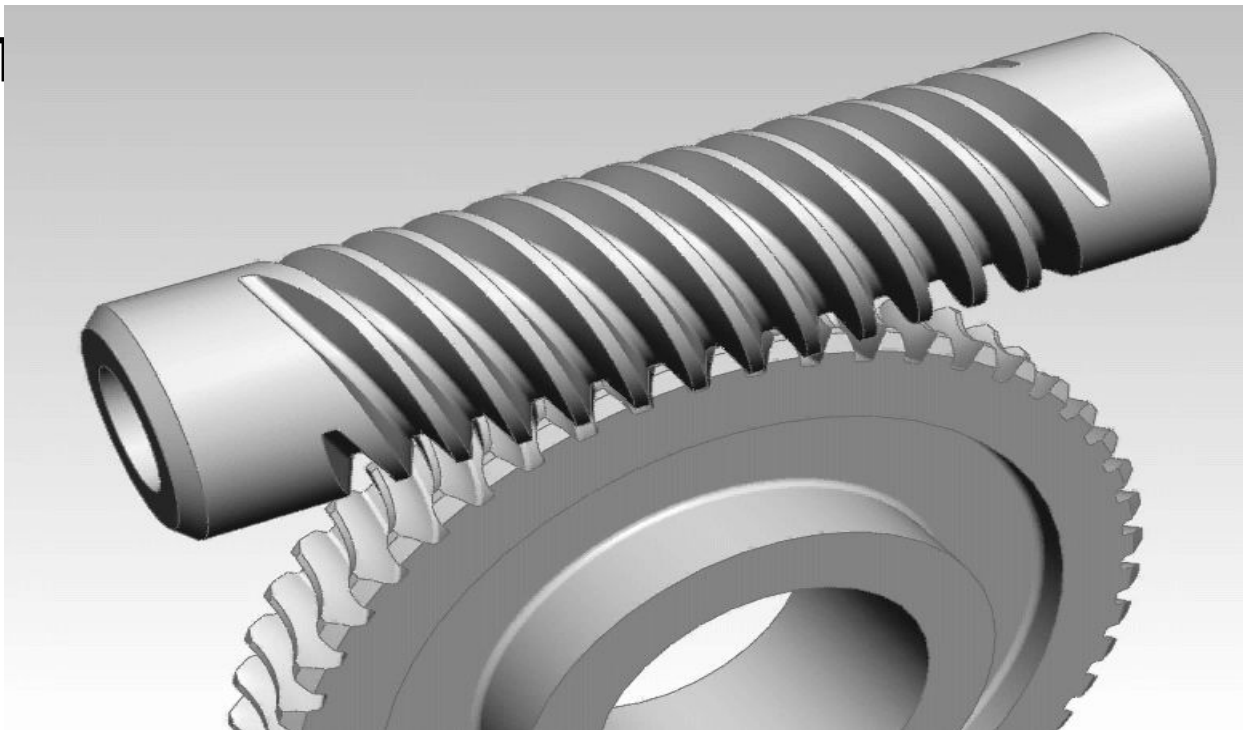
Типы зубчатых передач для вращательных движений:
